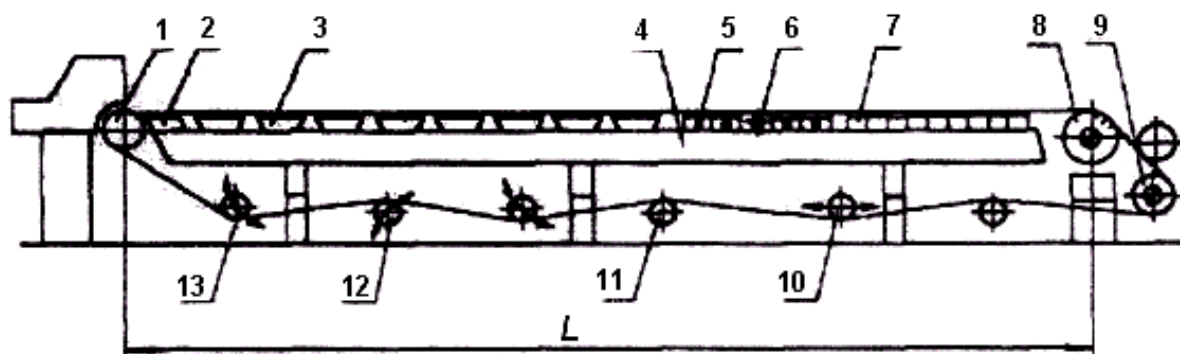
Сеточная часть с плоским столом: 1- грудной вал; 2 – формующий ящик; 3 – гидропланочный ящик; 4 – консольный стол; 5 – «мокрый» отсасывающий ящик; 6 – регистровый вал; 7 – отсасывающий ящик; 8 – отсасывающий гауч – вал; 9 – сеткоповоротный вал; 10 – сеткоправка; 11 – сетковедущий вал; 12 – сетконатяжка; 13 – измерительный вал
